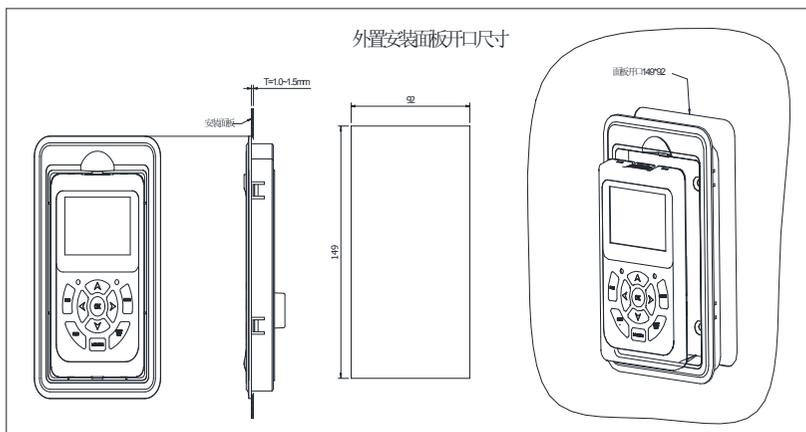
： 键盘安装开口尺寸图(尺寸单位：mm)
